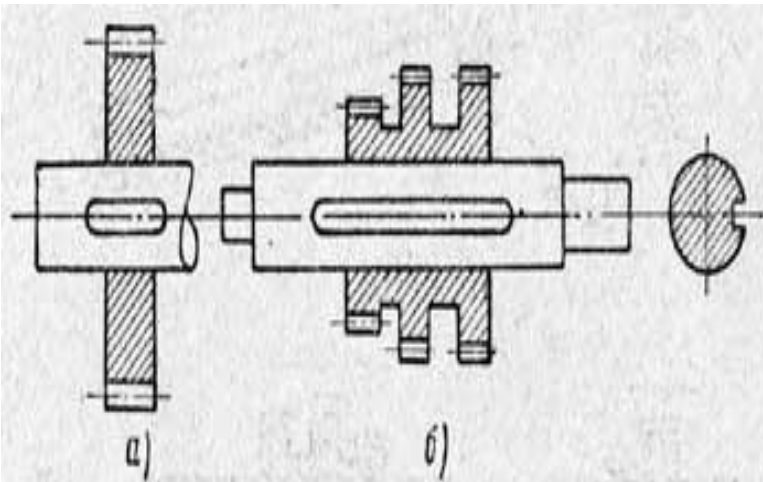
Соединение вала с зубчатым колесом (а) и блоком колес (б) при помощи призматической закладной шпонки
